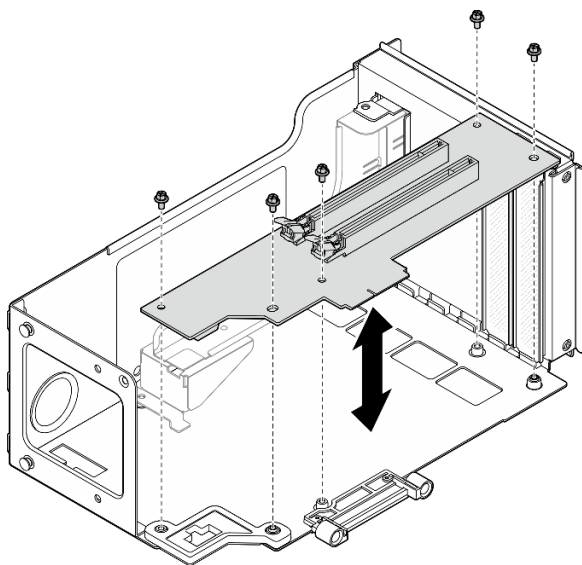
Removendo o cartão da placa riser PCIe da placa riser
